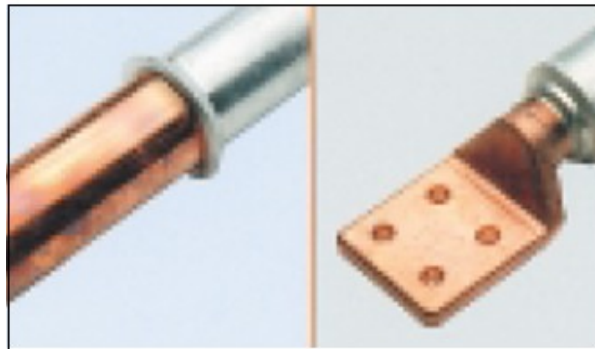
Aspectul macroscopic al unei îmbinări sudate prin frecare între un aliaj de aluminiu și un aliaj de cupru
